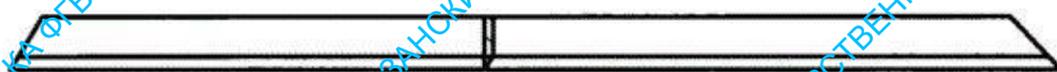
Заготовка для лезвия из полосовой среднеуглеродистой стали
